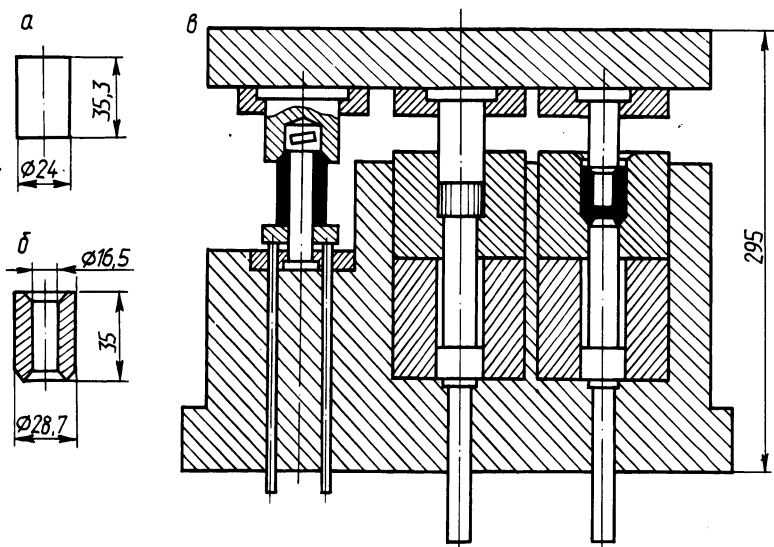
Заготовка (а) , поковка детали (б) и штамп для ее выдавливания (в)
